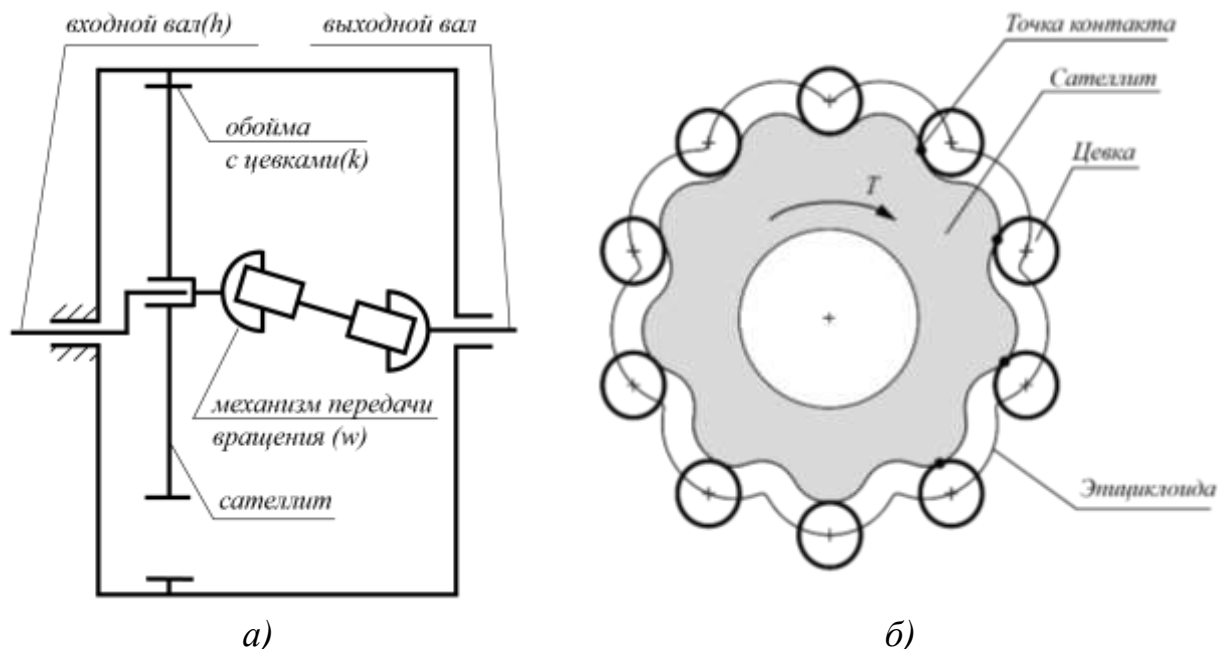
Кинематическая схема ПЦП (а) и внешний вид планетарно-цевочной передачи (б)
